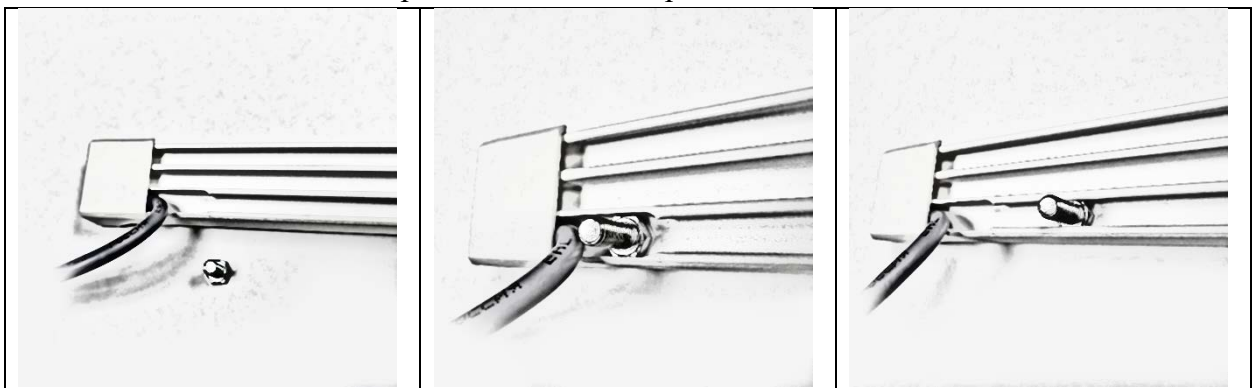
Установка крепежного болта М5 на корпус светильника.
